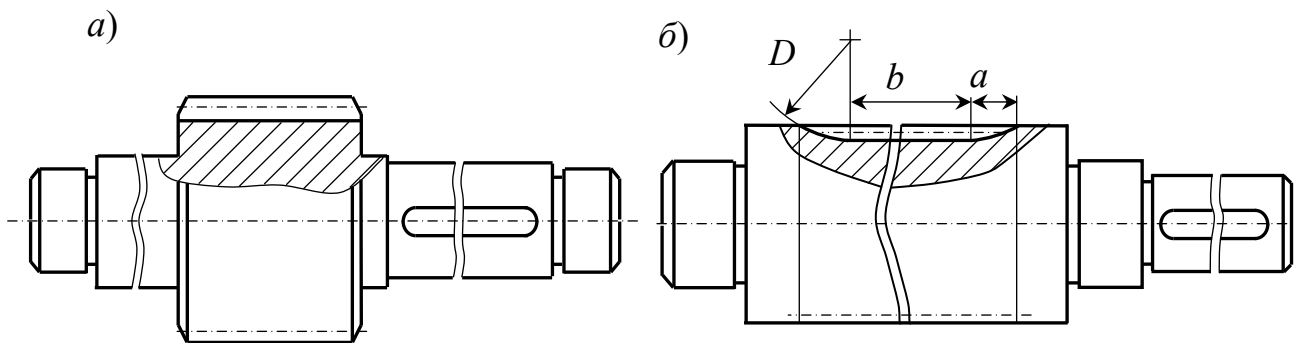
Вал-шестірні: а – зубці нарізані на виступаючому вінці; зубці заглиблені у тіло вала
